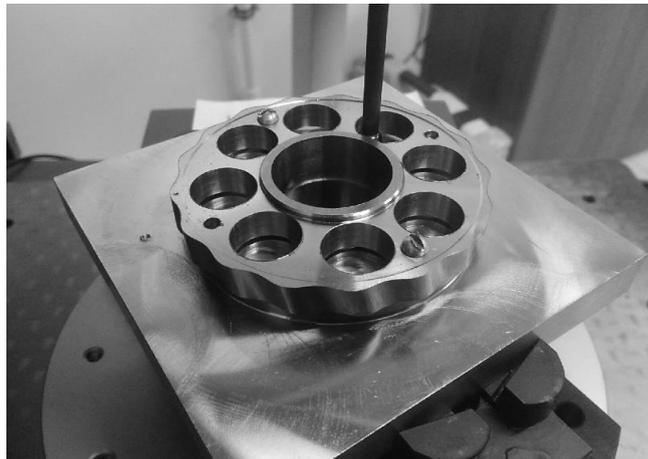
Метрологический контроль точности обработки сателлита циклоидального редуктора с косозубым зацеплением зубчатых колес
